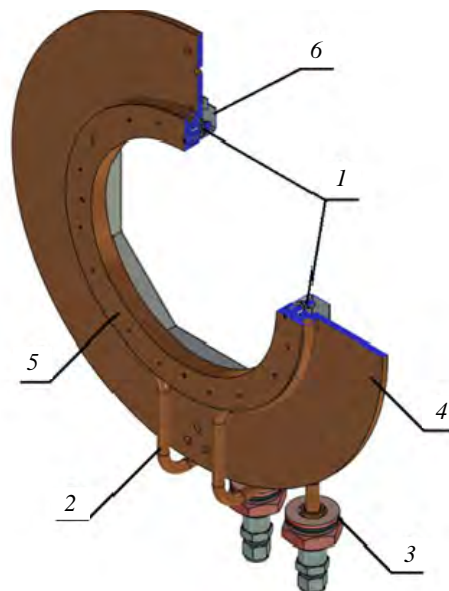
Общий вид прицельного устройства, основные элементы: 1 — вторично-эмиссионные датчики; 2 — трубка охлаждения; 3 — развязка вакуум—атмосфера; 4 — диск; 5 — корпус датчиков; 6 — экран
